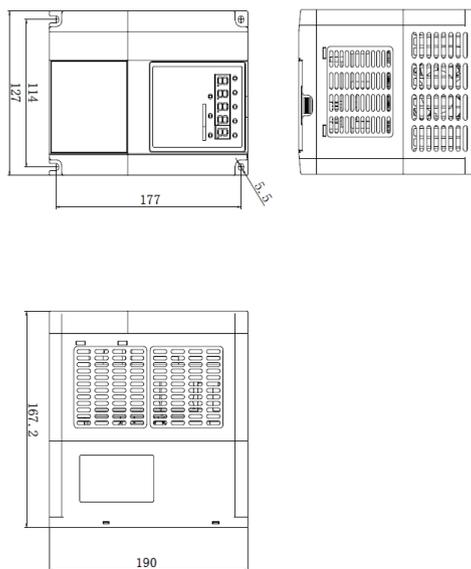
2.2~3.7kW 外型尺寸及安装尺寸示意图
